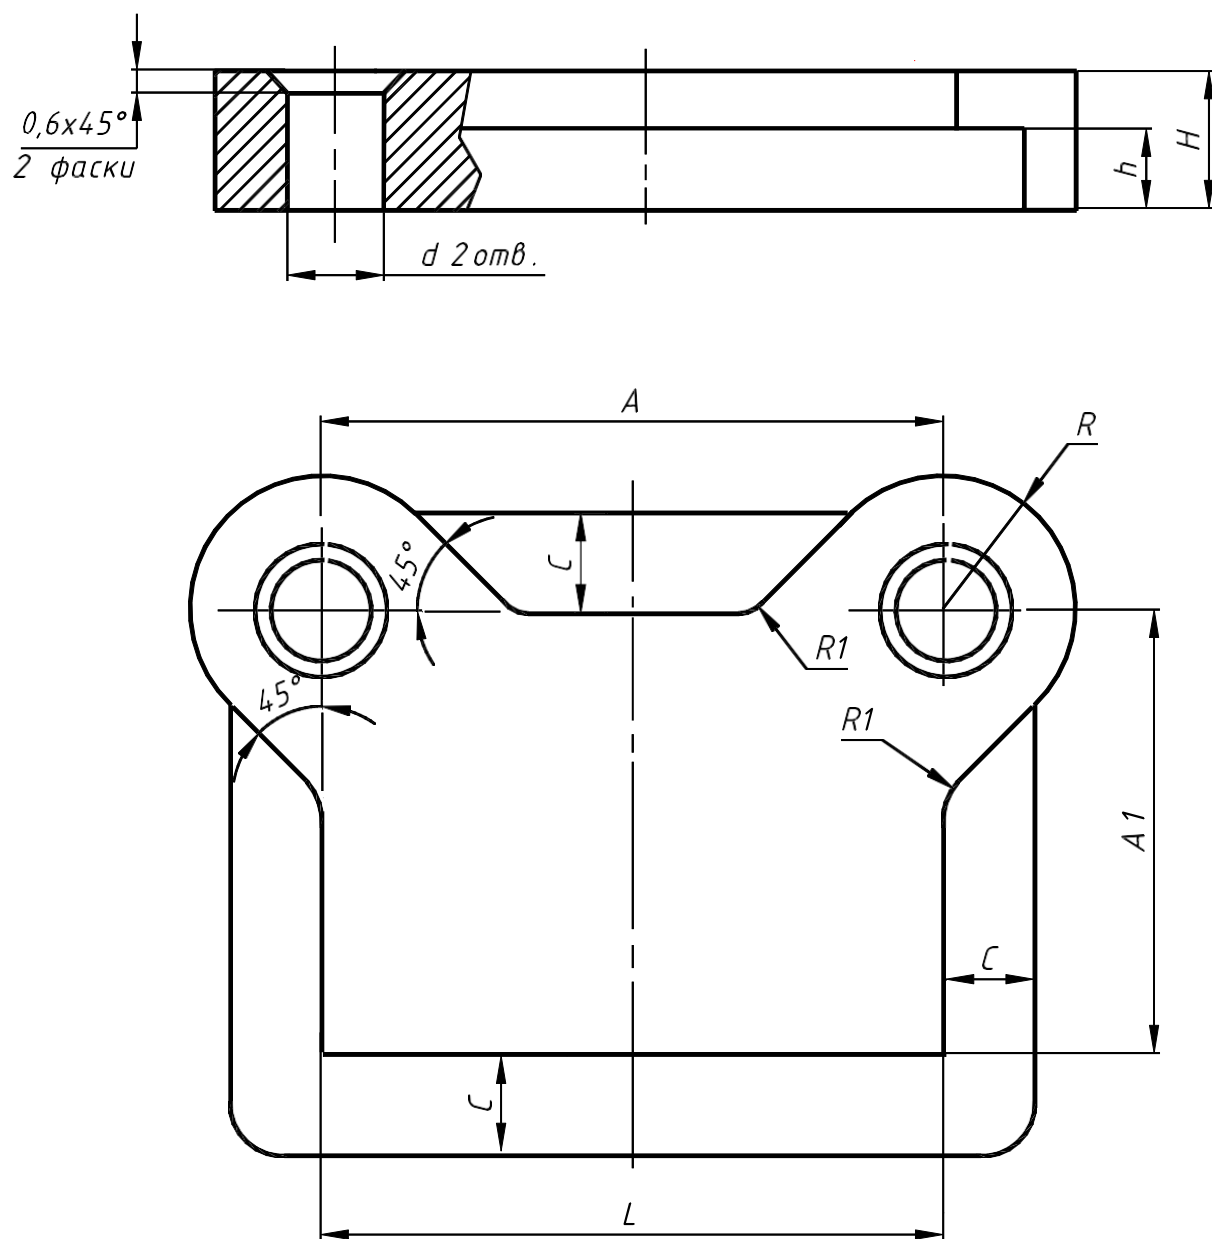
Чертеж с параметрами нижней плиты блока штампа
